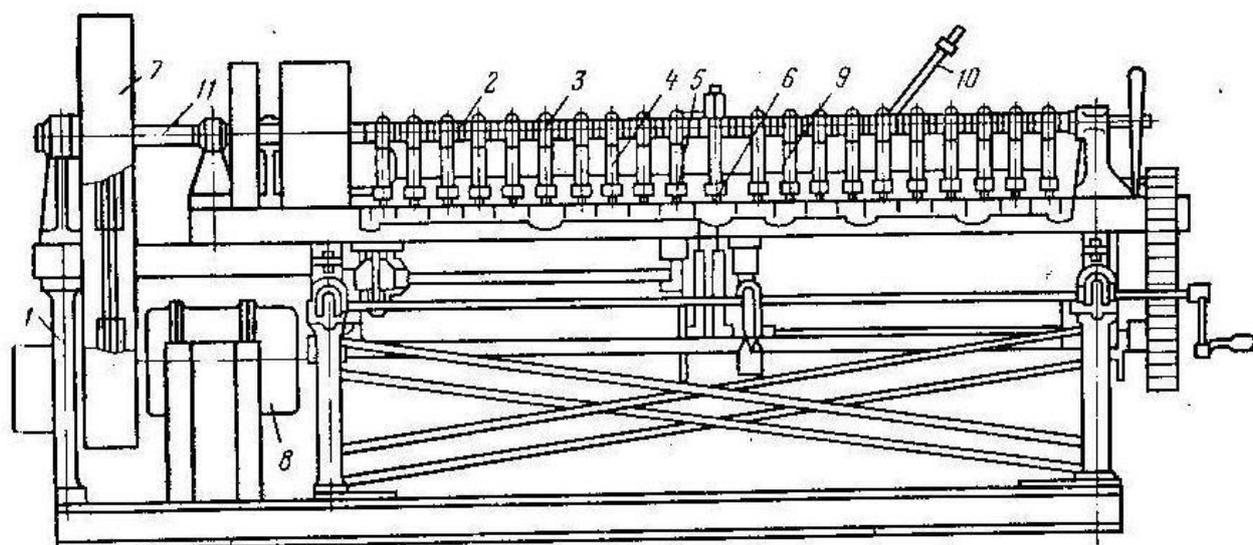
Схема универсальной автоматической многошпиндельной пилоточки ПТА
